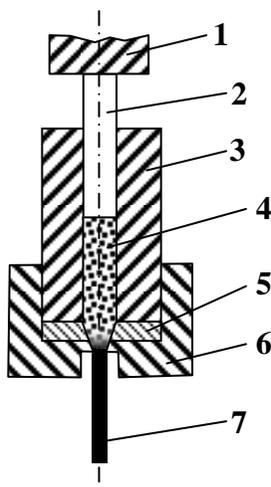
Схема мундштучного прессования: 1 – плунжер гидравлического пресса; 2 – пуансон; 3 – стальной стакан; 4 – порошок; 5 – мундштук; 6 – матрица; 7 – заготовка
